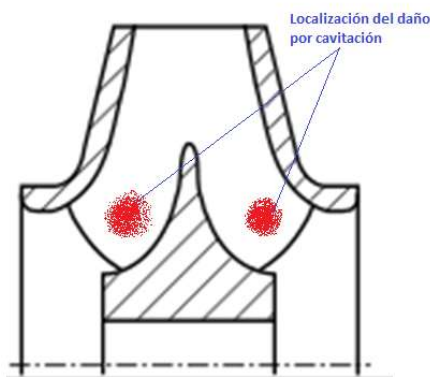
Ubicación del Daño (corte longitudinal) [1]
